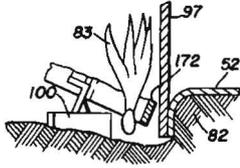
Schnittdarstellung quer zur Furche zum Pflanzvorgang mit dem Gerät nach Bild 12
